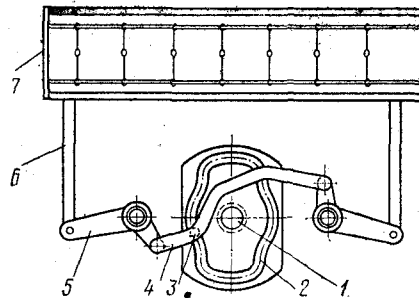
Схема кулачкового зверообразовательного механизма бесчелночного станка П-125-А
